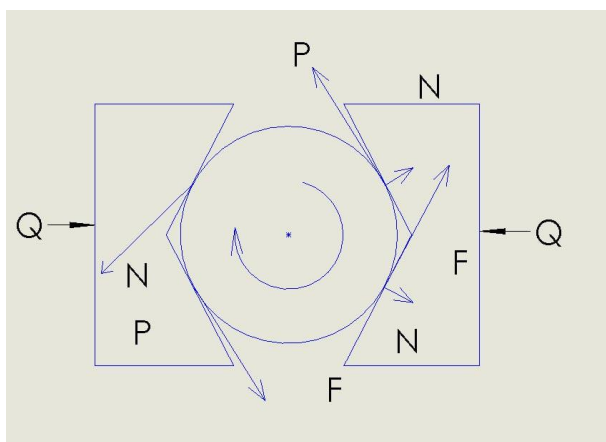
сили які діють на деталь під час свердління
